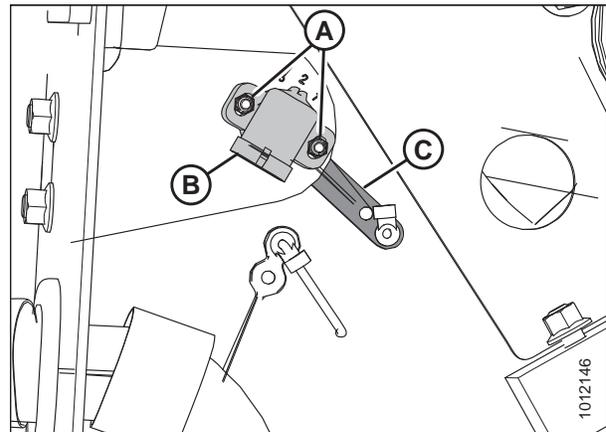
Ensamble del sensor de altura de la plataforma; lado izquierdo
